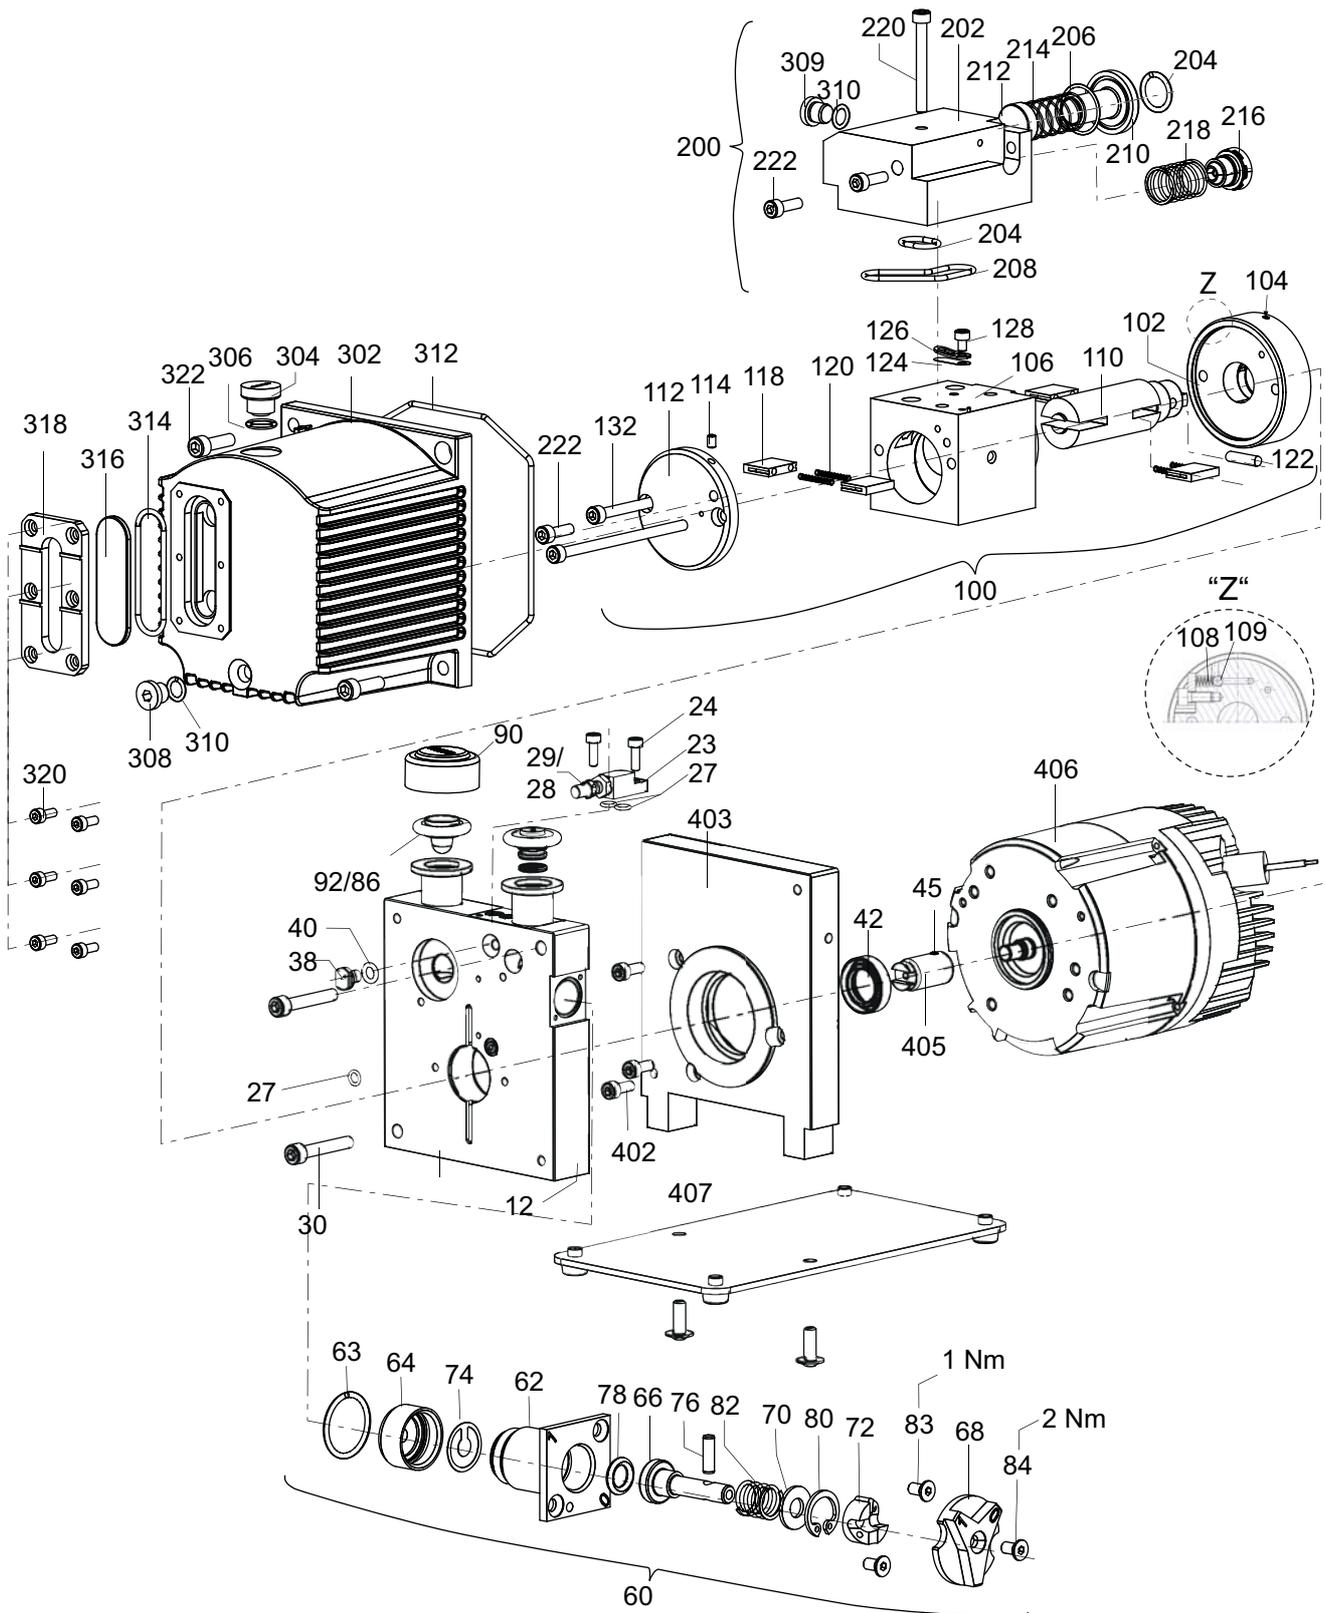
Explosionszeichnung DUO 3 DC / DUO 3 M DC
